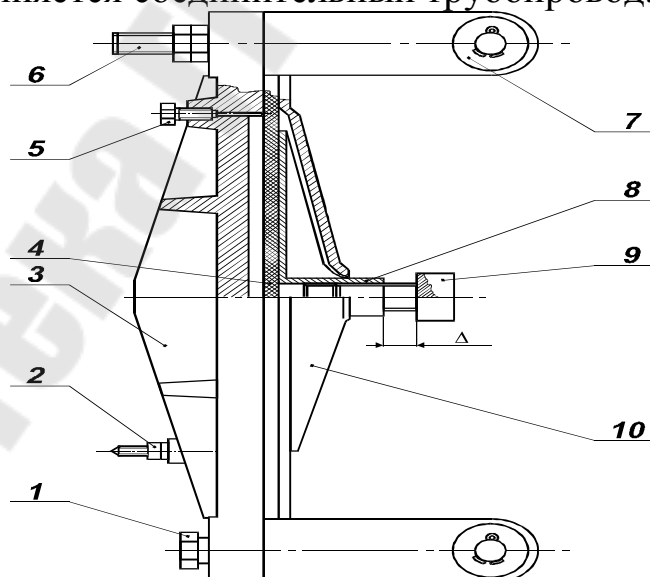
Трансформатор давления: 1 – болт; 2 – штуцер; 3 – корпус; 4 – мембрана; 5 – пробка; 6 – шпилька; 7 – обойма; 8 – поплавок; 9 – упор; 10 – крышка
